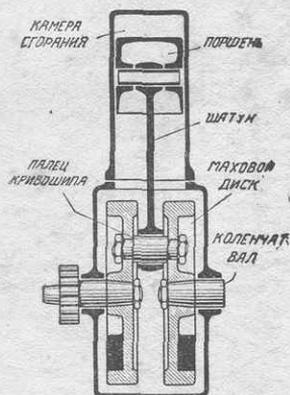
Схематический разрез одноцилиндрового двигателя.
